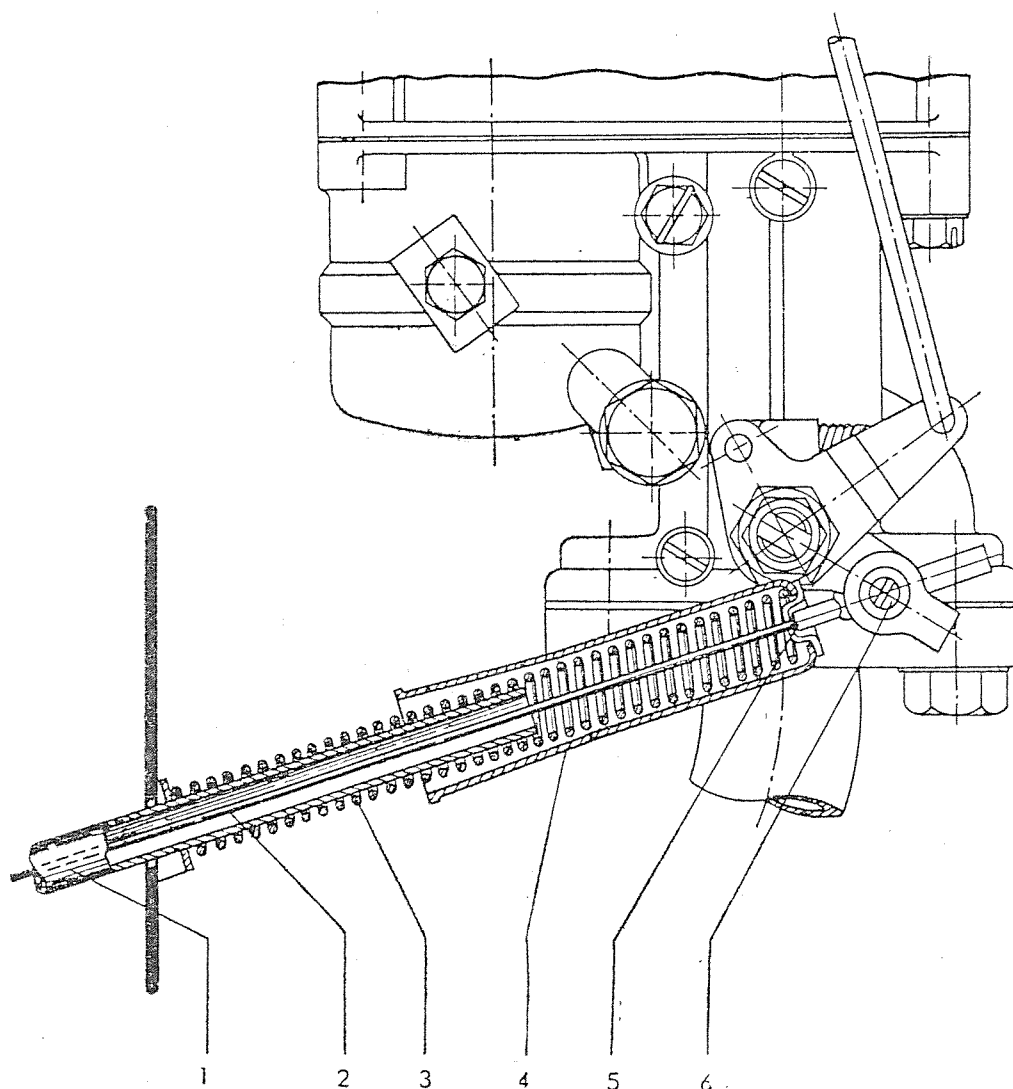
Montaje del tubo guía para el tiro del carburador.
